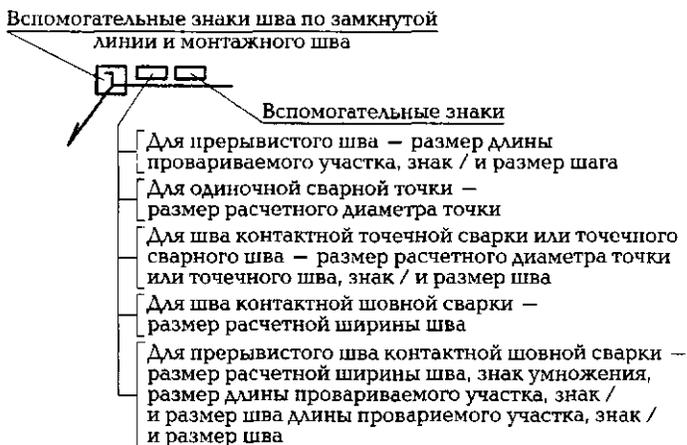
Структура условного обозначения нестандартного шва или нестандартной одиночной сварной точки
